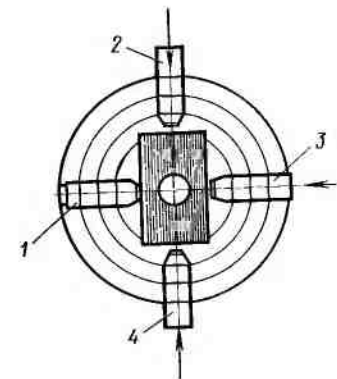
Установка заготовки в четырехкулачковом патроне
